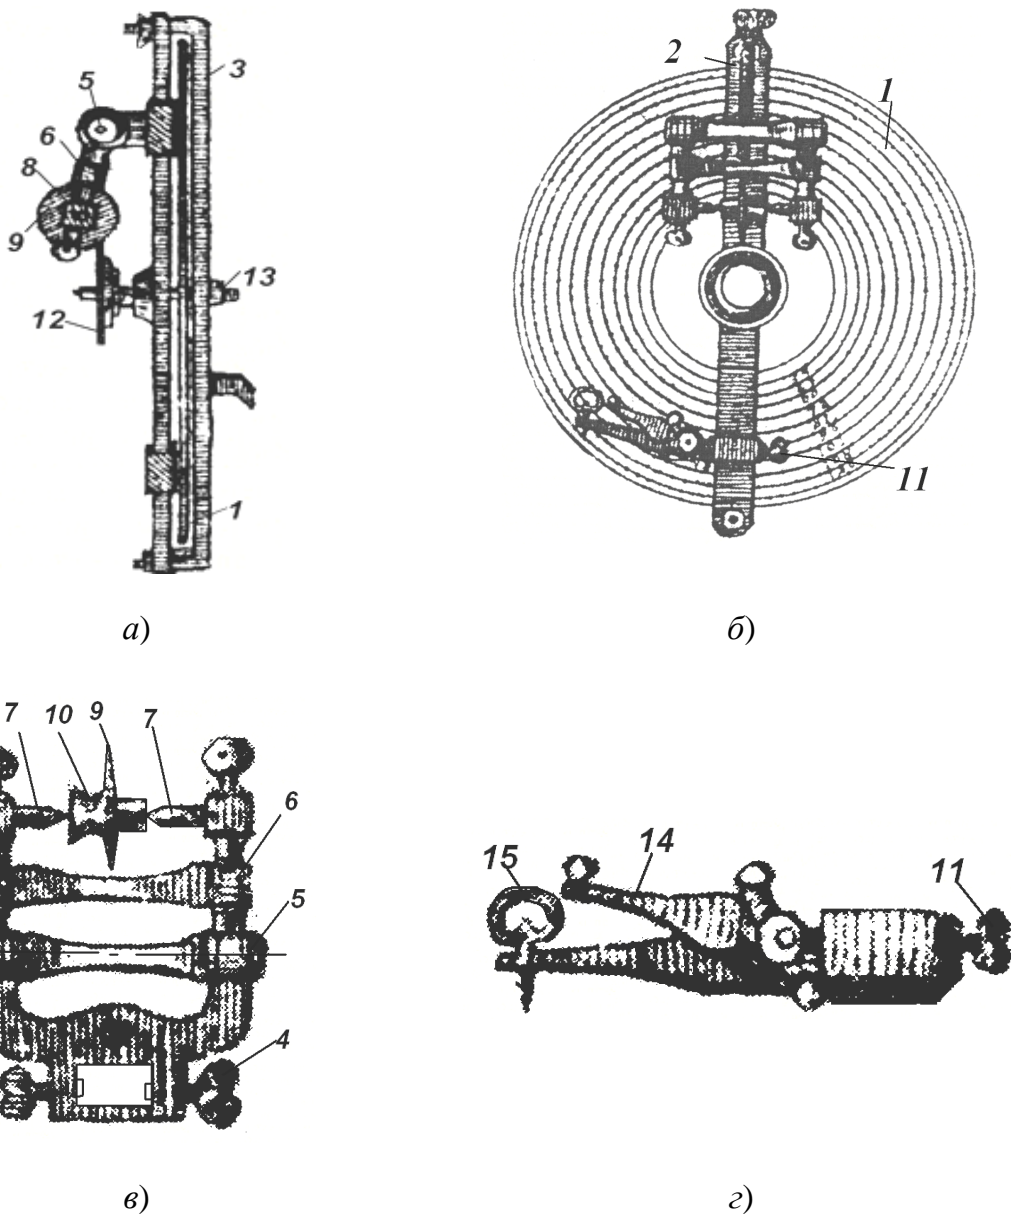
Устройство для фрезерования часовых зубчатых колес (по Н. Биону, начало 18 в.)
